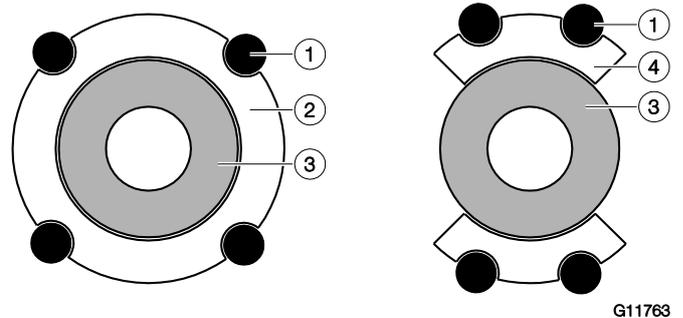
Zentrierung der Zwischenflanschausführung mit Ring bzw. Segment
